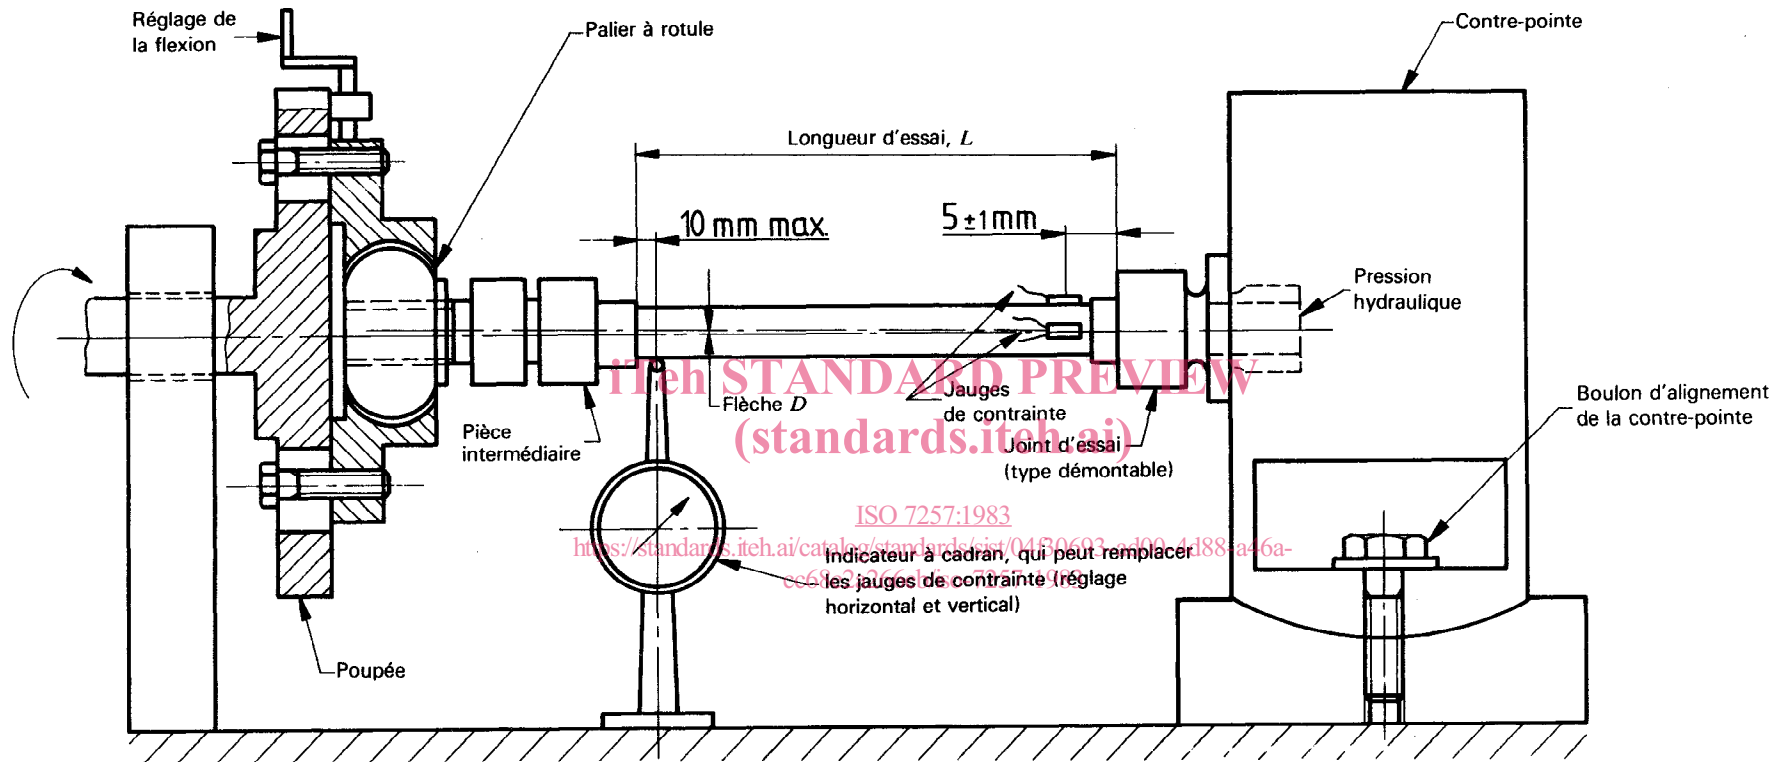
Schéma type d'une machine d'essai de flexion rotative
